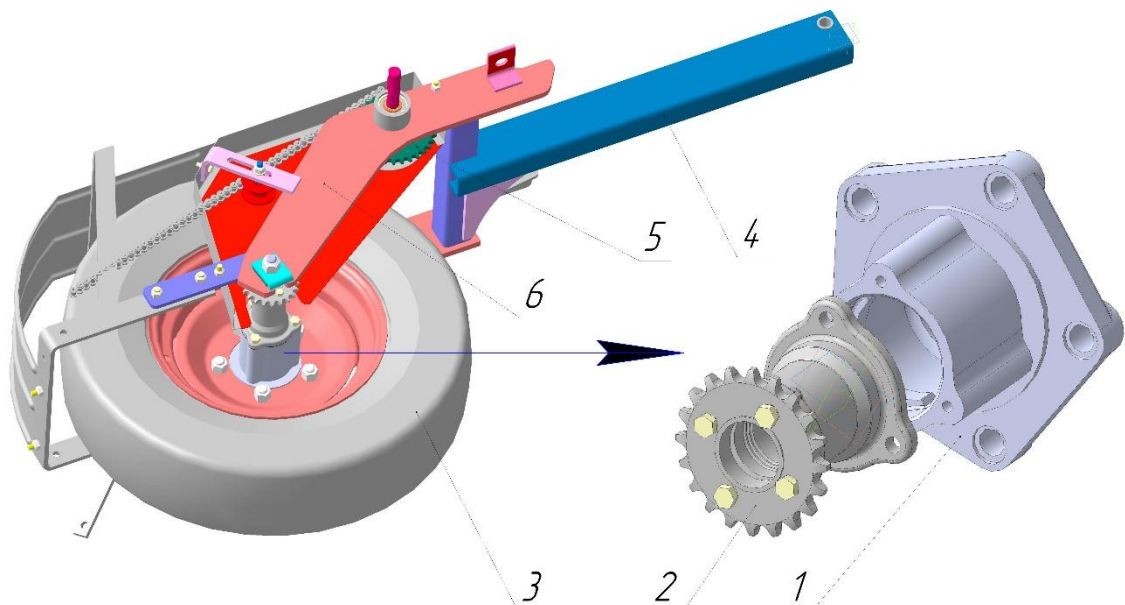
Опорно-приводне колесо з механізмом передач
